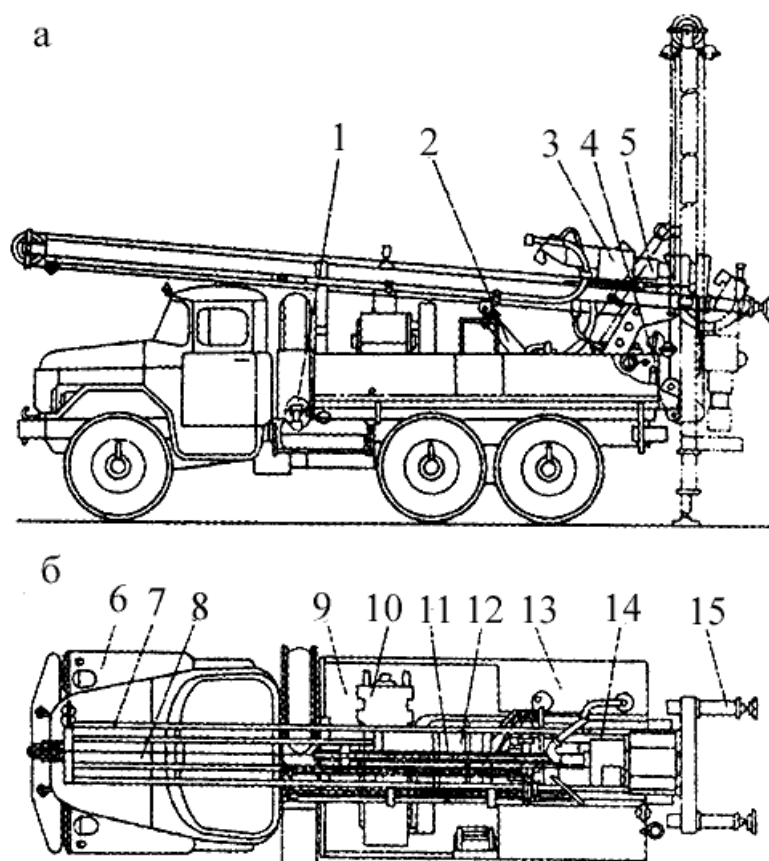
Схема буровой установки УРБ-2А-2: а - вид сбоку; б - вид сверху; 1 - коробка отбора мощности; 2 - цилиндр подъема мачты; 3 - вращатель; 4 - пульт управления; 5 - элеватор для труб и патрон для шнеков; 6 - автомобиль; 7 - мачта; 8 - талевая система; 9 - рама; 10 - установки бурового насоса и компрессора; 11 - гидродомкрат подачи; 12 - раздаточная коробка; 13 - обвязка гидросистемы; 14 - каретка; 15 - опорный домкрат.
